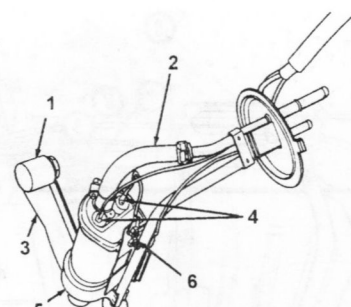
б Сборка топливного насоса и посылающего устройства на автомобилях с СМВ
